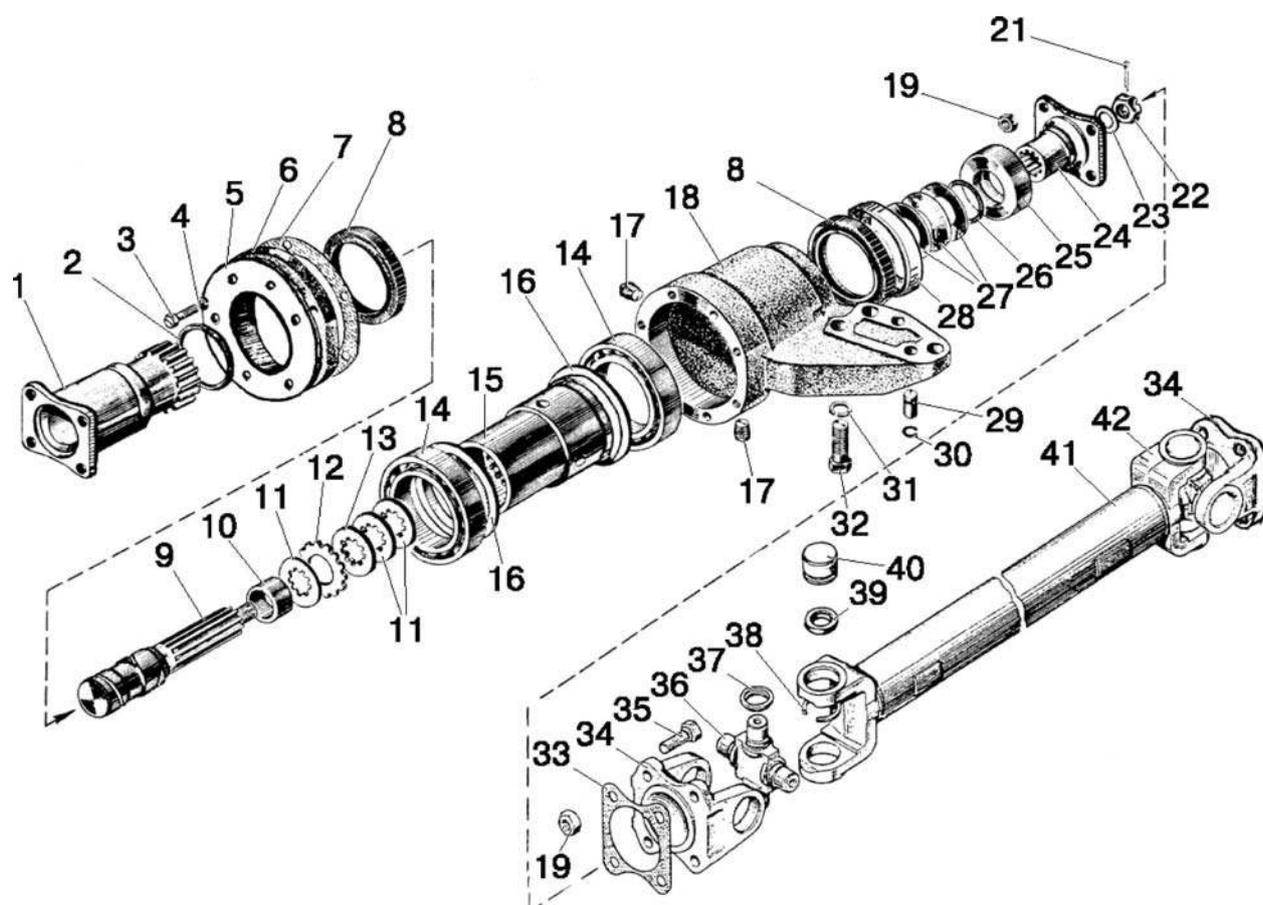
Привод карданный. Промежуточная опора карданного вала
